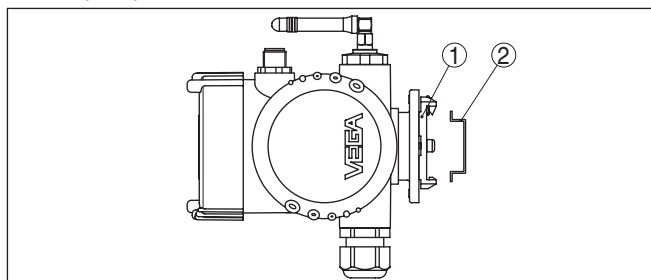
PLICSMOBILE T61 для монтажа на несущей рейке
